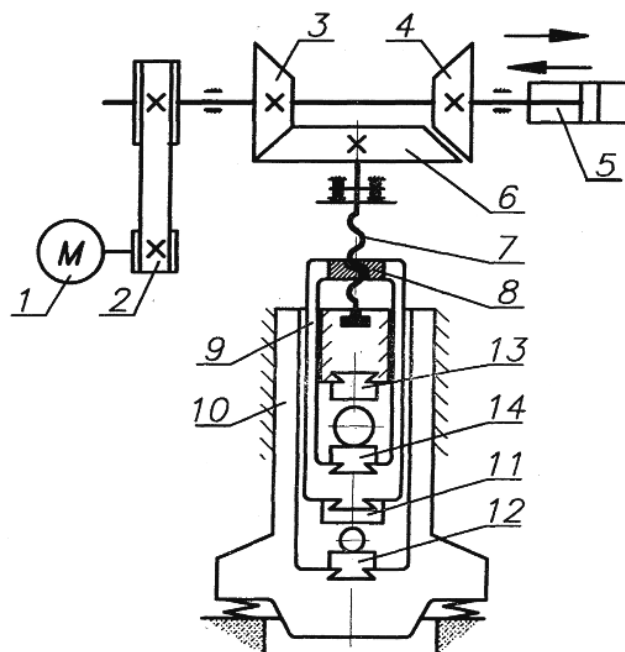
Гвинтовий фрикційний двоопераційний штампувальний прес без зворотного ходу
